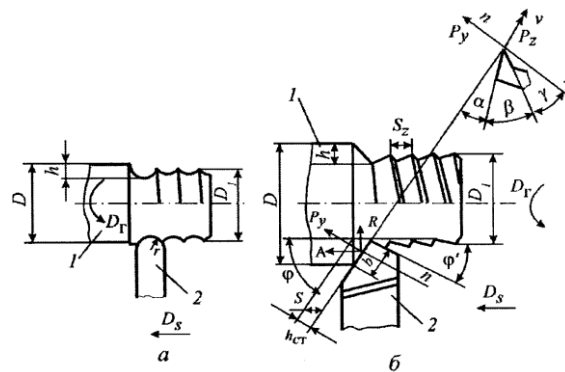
Схеми поздовжнього точіння: а - чорнового; б - чистового; 1 - заготівка; 2 – токарний різець
